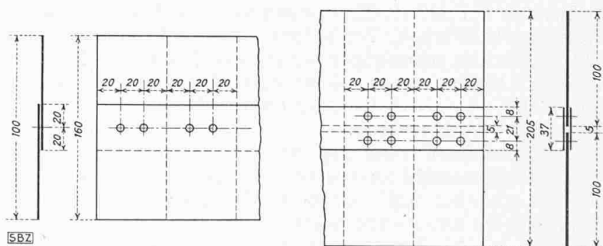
Ausführung von Schweißproben, links A, rechts B
